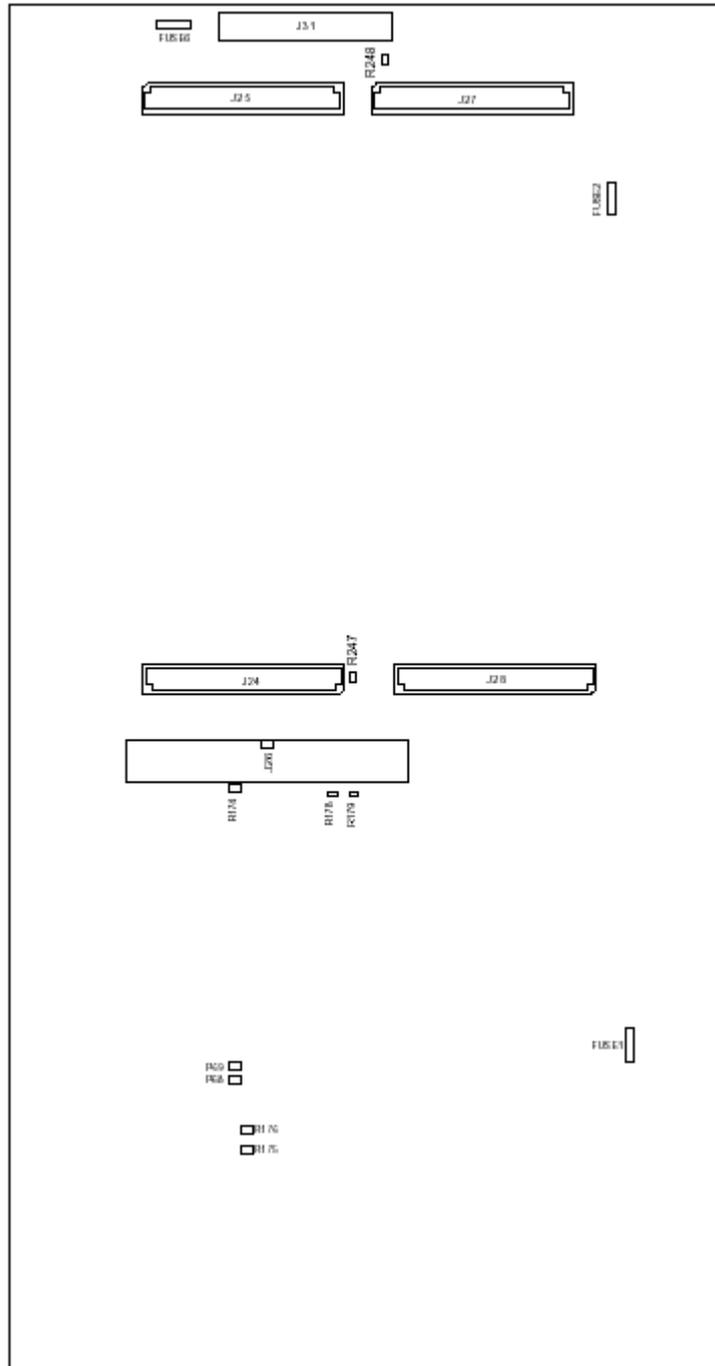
Layout lato saldature di connettori, ponticelli, Led e fusibili
